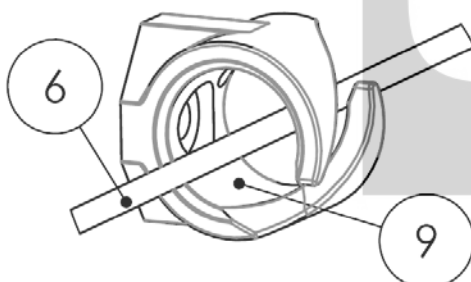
Método de montaje del cable a través de un punto de anclaje intermedio.
